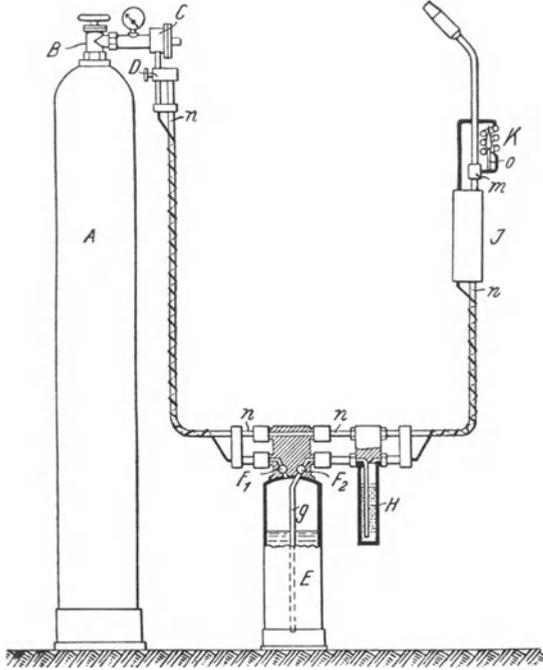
Benzolschweißanlage älterer Bauart.
